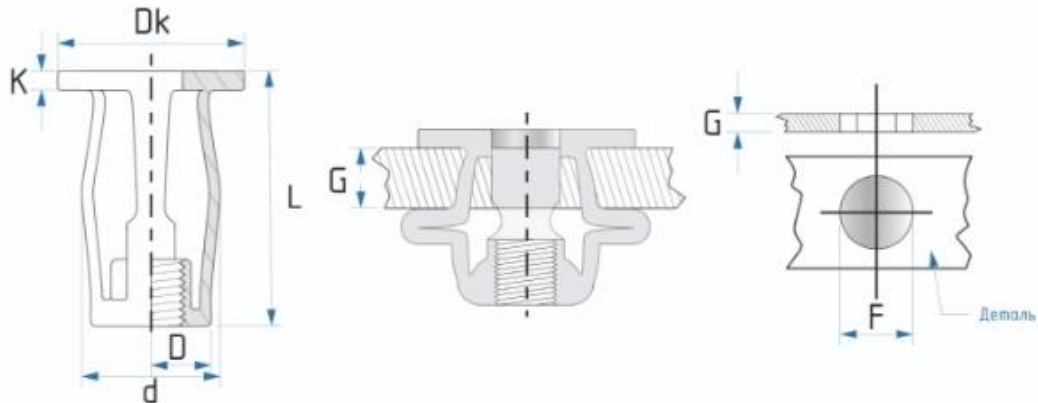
а - Заклёпка резьбовая, лепестковая, стандартный борт
